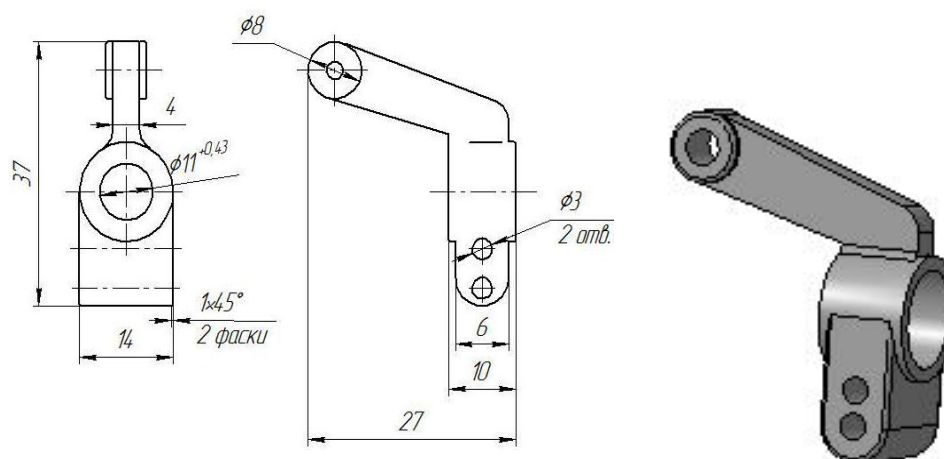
Чертеж и 3D-модель ступицы заднего колеса
